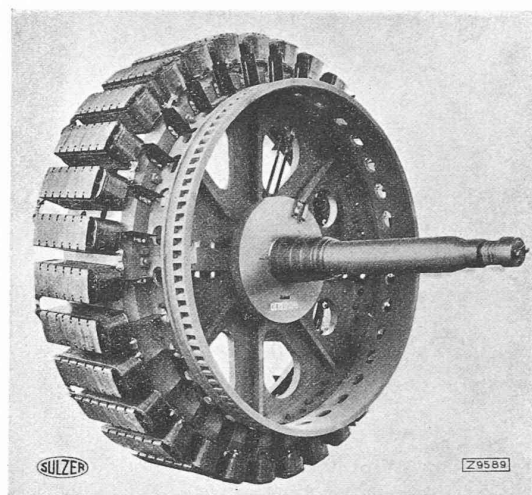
Rotor de l'alternateur de 5000 kW.
